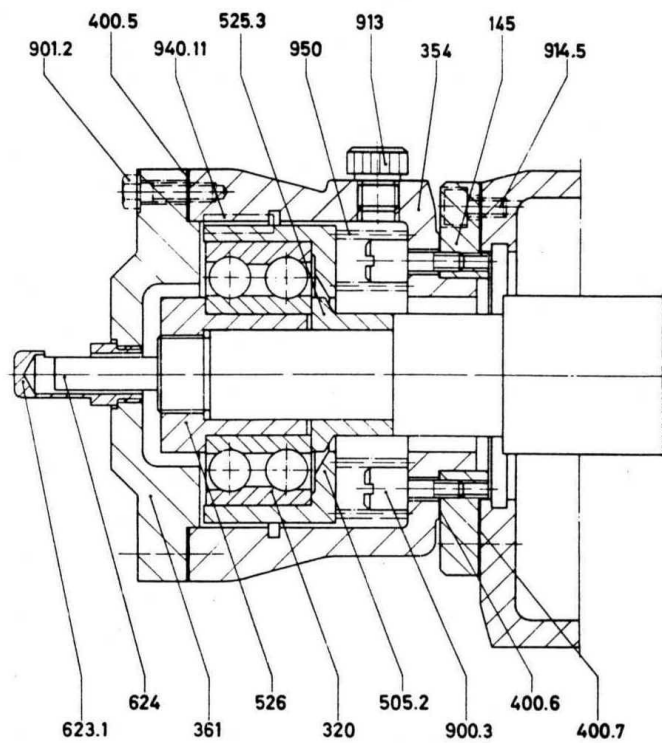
Dispositivo de compensação do empuxo axial com rolamento
